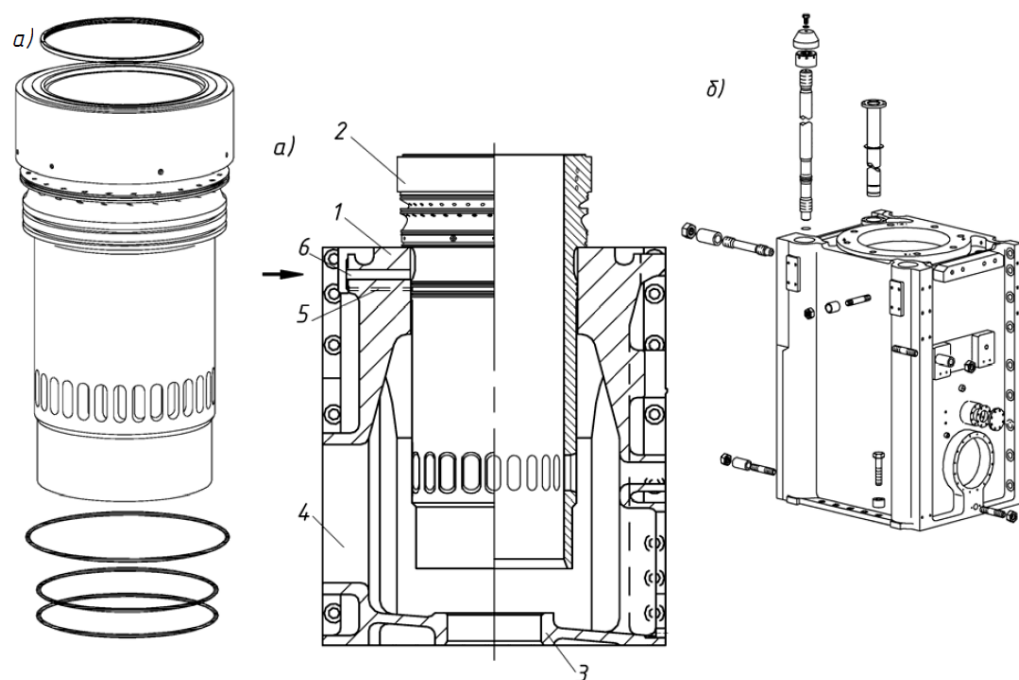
Робочий циліндр і сорочка охолодження дизеля 6G40ME-C9.5
